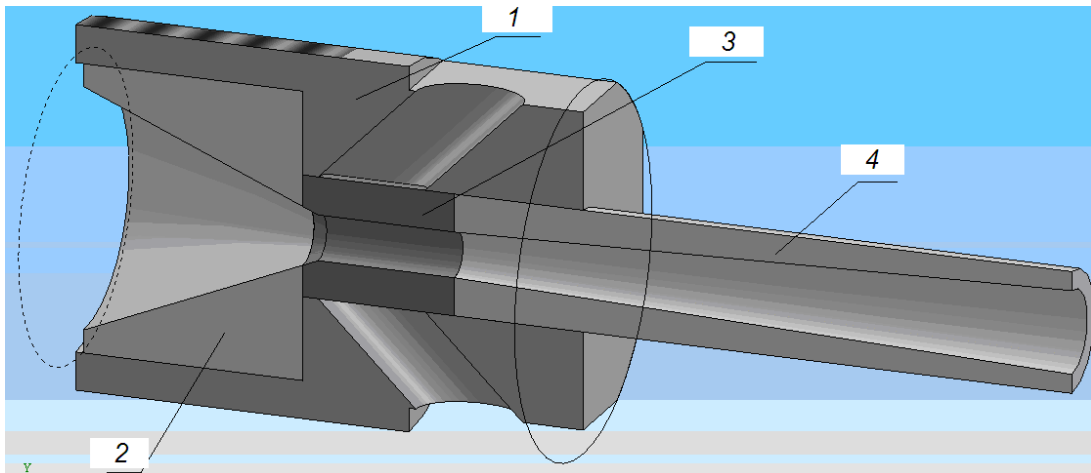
САПР модель основних частин нової конструкції сопла абразивоструменевої машини. (1 – корпус; 2 - широкий конічний вхід; 3 - пориста циліндричні трубчаста вставка; 4 - вузький довгий конічний вихід).
